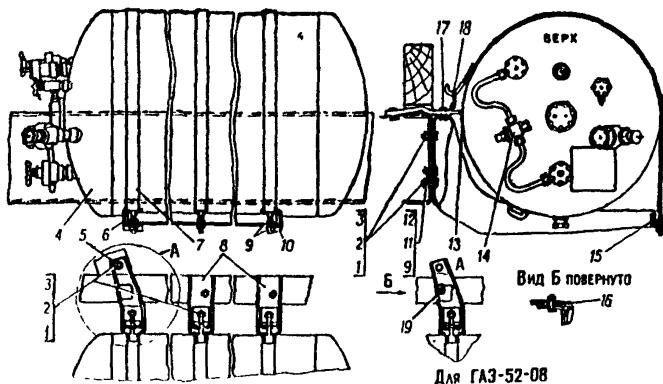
Установка баллона на автомобилях ГАЗ-53-07 и ГАЗ-52-08
